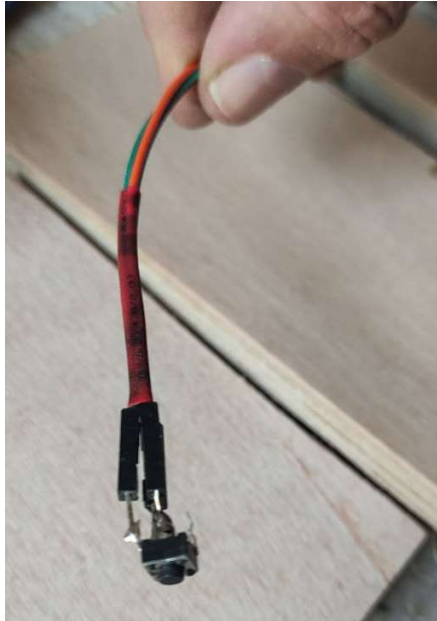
Botón con cables soldados y tubo termorretráctil.
